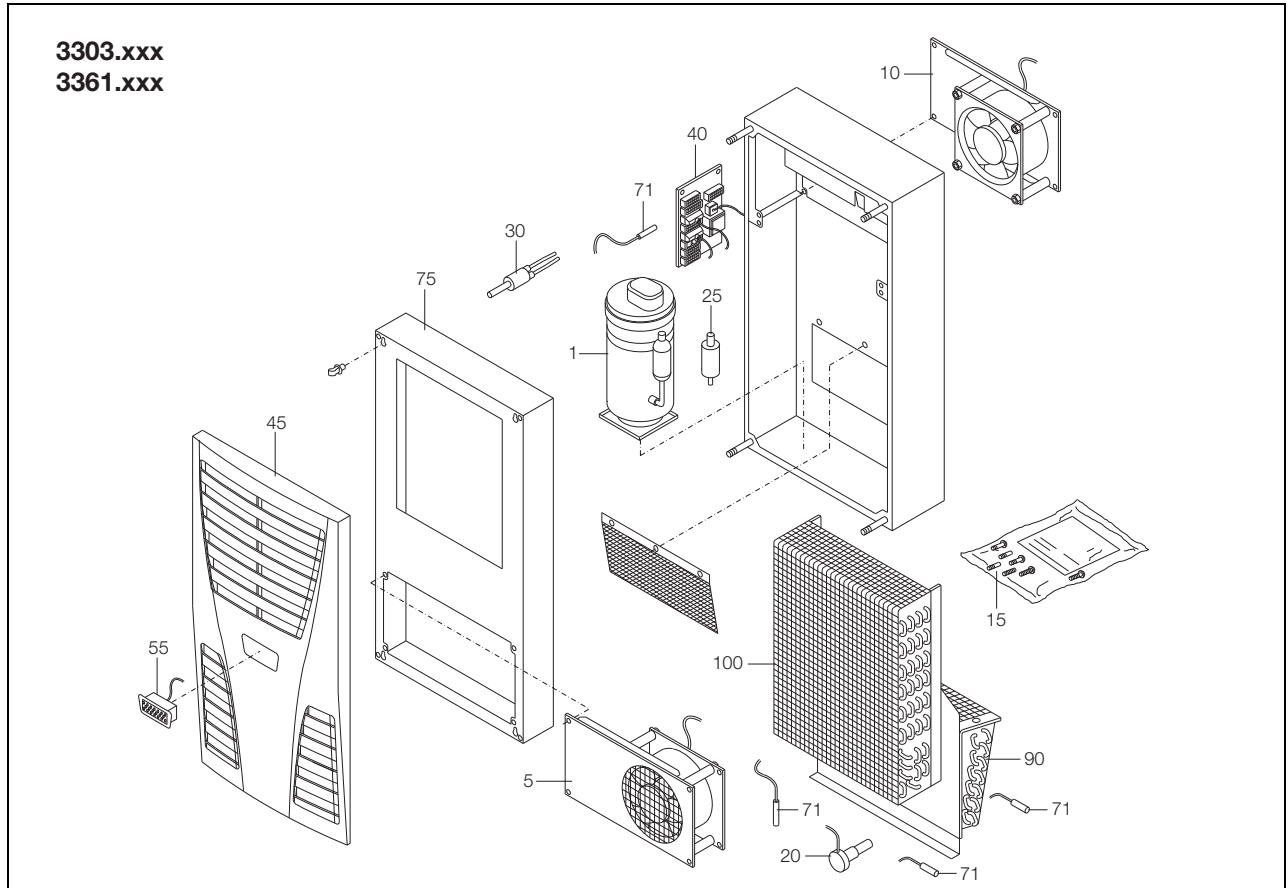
Pièces de rechange 3303.xxx, 3361.xxx
